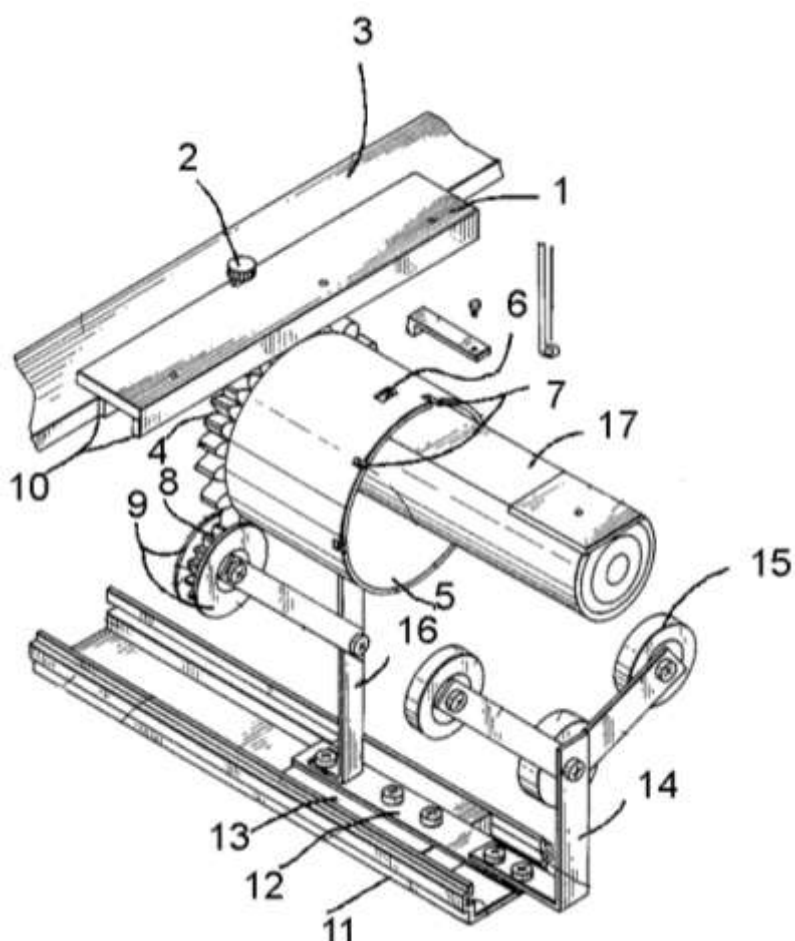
Каретка координатного устройства с приспособлением для вышивки на готовых изделиях
